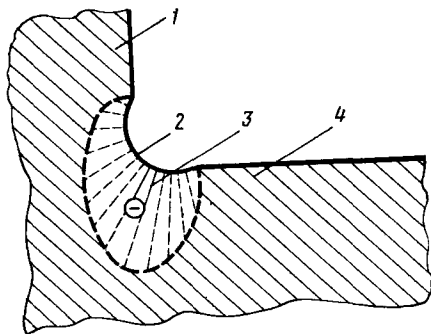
Эпюра сжимающих напряжений в галтели шейки коленчатого вала, создаваемых накатыванием:
